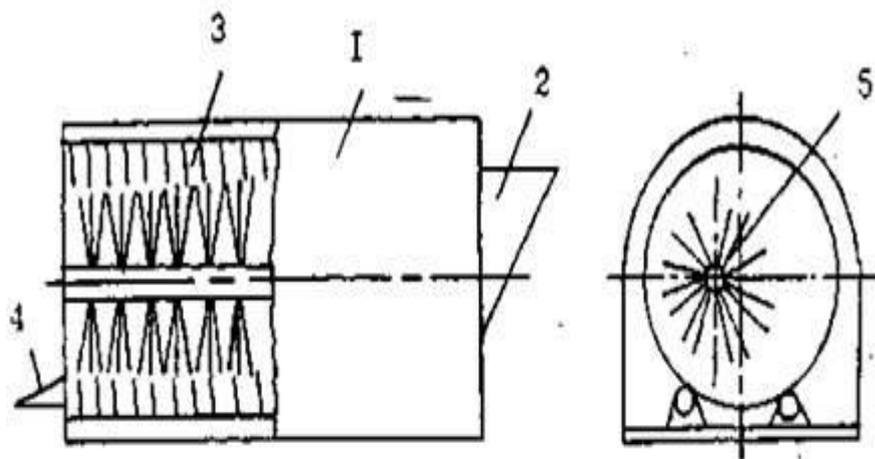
Схема барабанно-щеточной конструкции ВИЭСХ очистителя корнеплодов. 1 - корпус; 2 - бункер загрузочный; 3 - обрешетка наклонная; 4 - горловина выгрузная; 5 - щетка синтетическая
